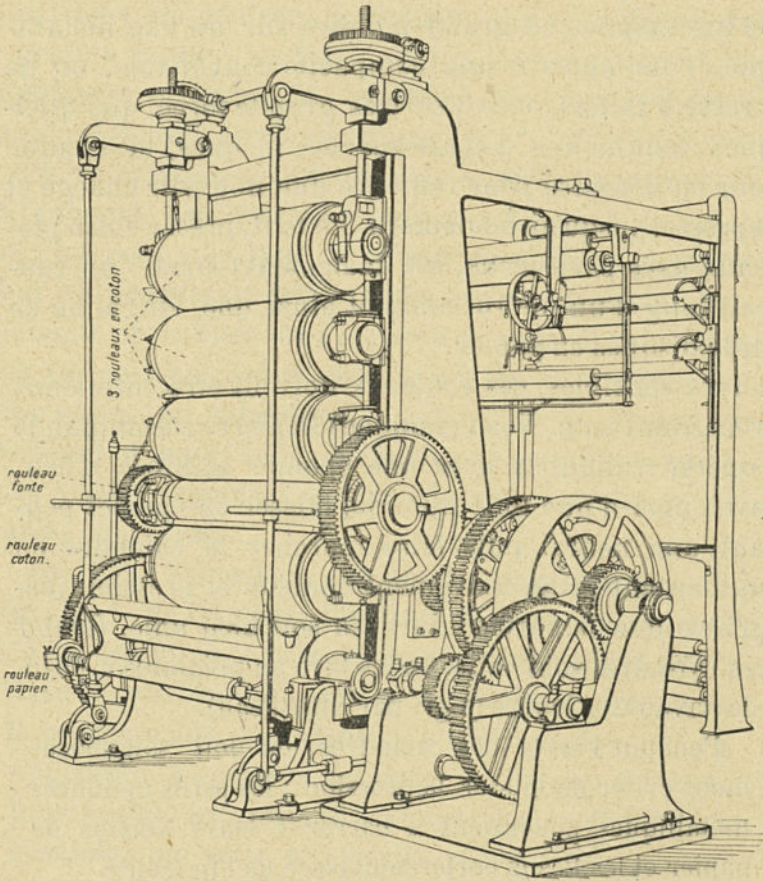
Calandre moderne à six rouleaux pour cylindrer, frictionner et beetler (Weisbach).
